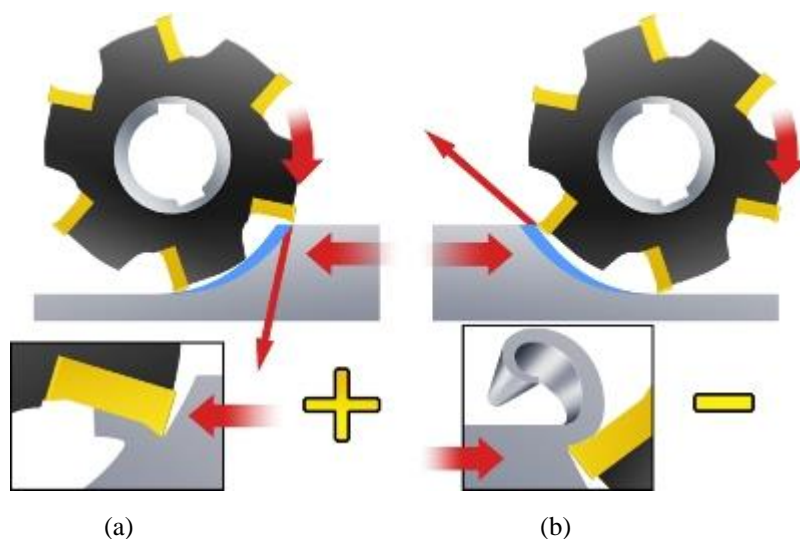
Maquinagem concordante e discordante: Corte Concordante (*Climb milling*) (a); Corte Discordante (*Conventional milling*) (b).
